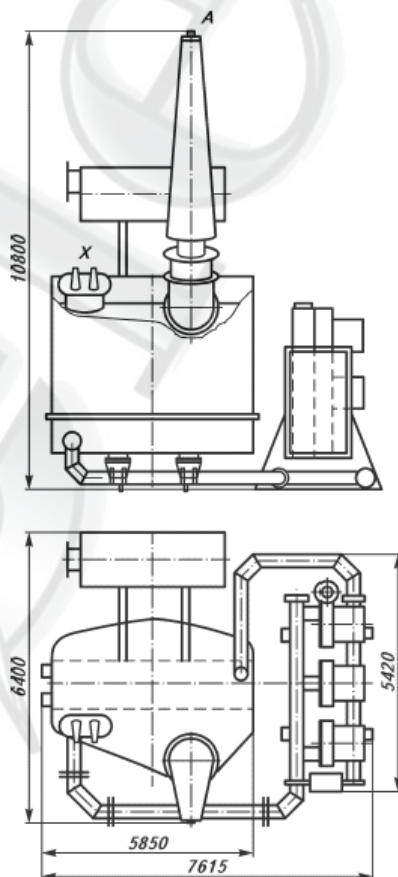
Общий вид и габаритные размеры реактора типа РОДЦ-110 000/750-У1
